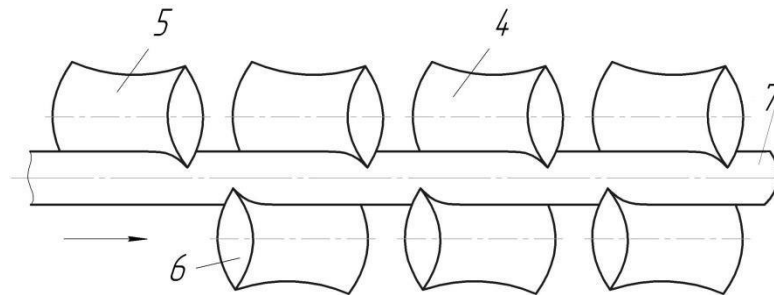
Схема багаторазового пружно пластичного вигину на валковому стані: 4 – верхній валок; 5 – спрямовуючий валок; 6 – нижній валок; 7 – труба
